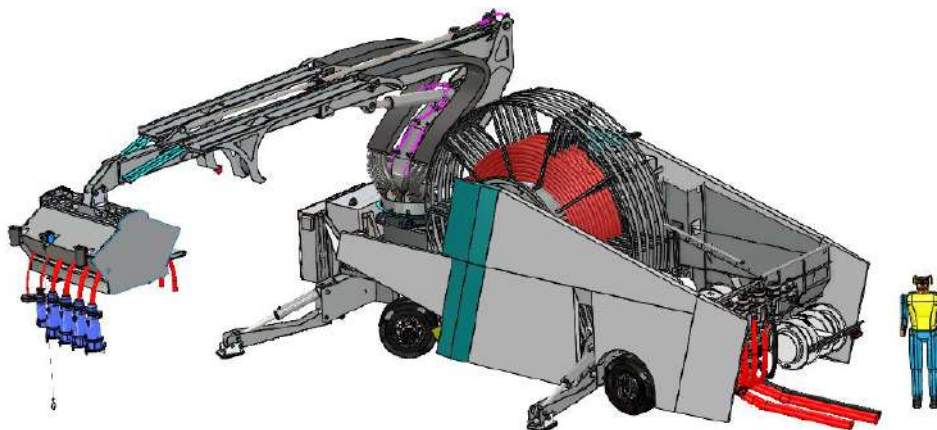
Concept design - Vista laterale sistema CMS Shorelink con braccio aperto
